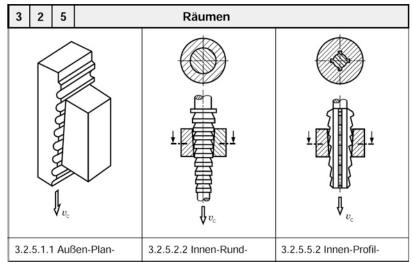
Plan-, Rund- und Profilräumverfahren / Procedee de broşare plană, cilindrică, profilată [WES 10]
